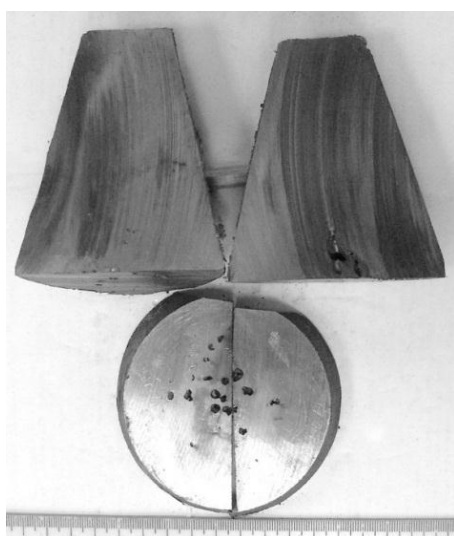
Вид усадочных раковин в образце пробы из супердуплексной стали
